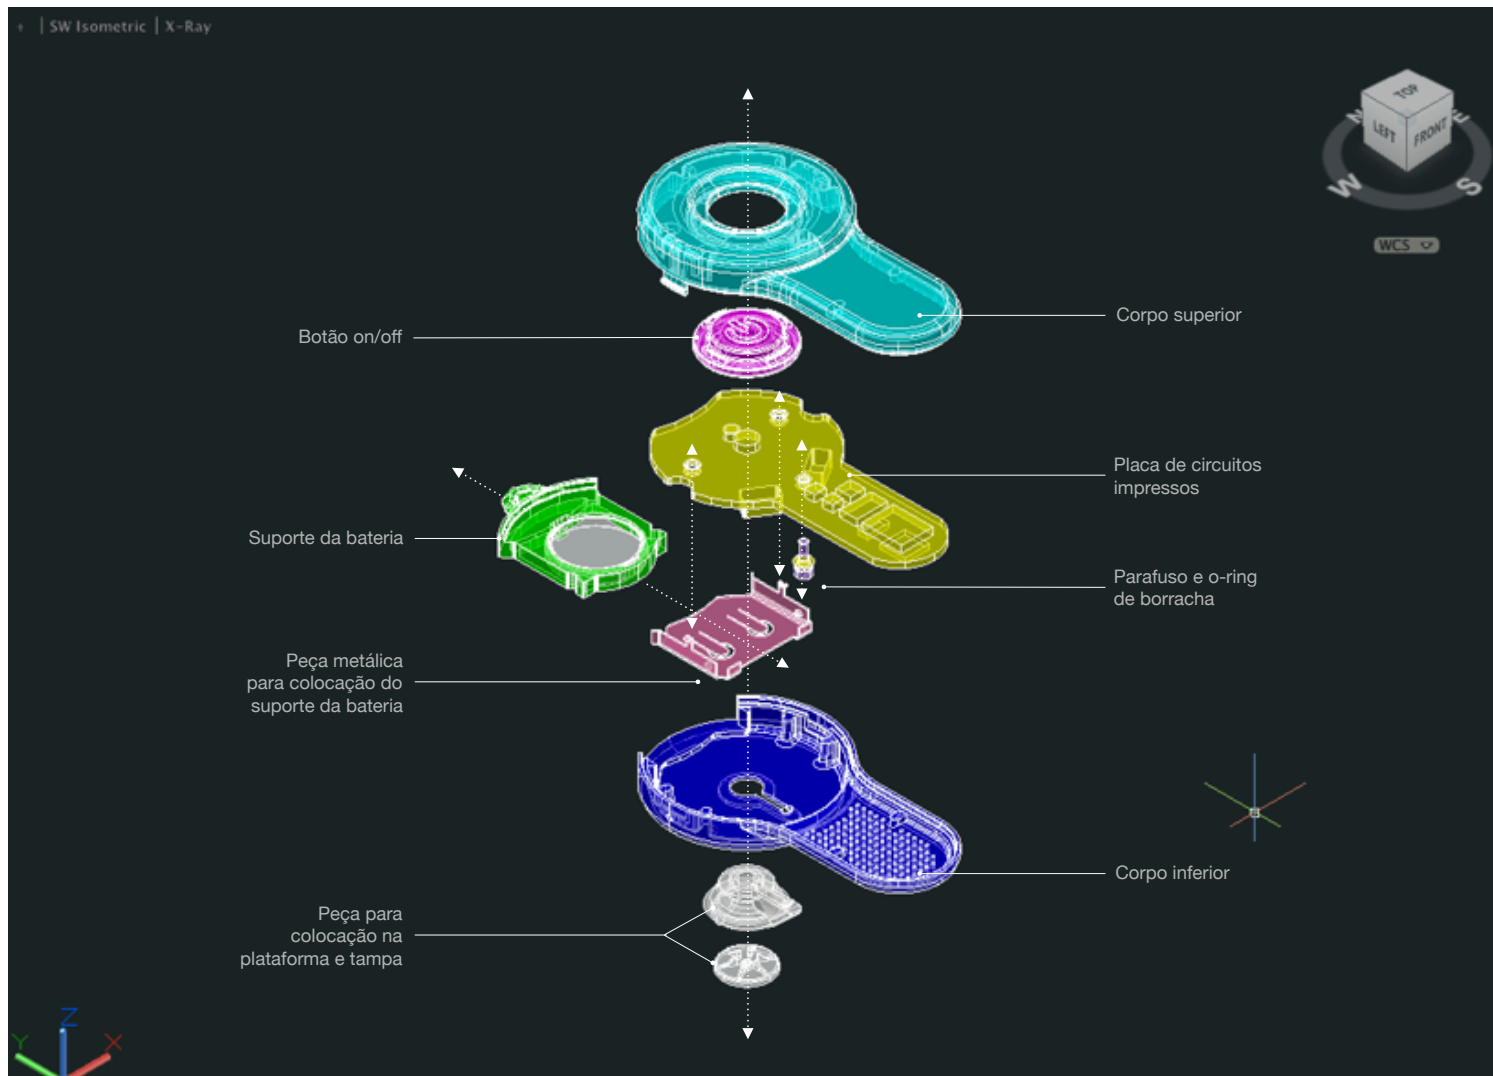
Axonometria CAD 3D explodida para visualização de todos os componentes do sensor.
